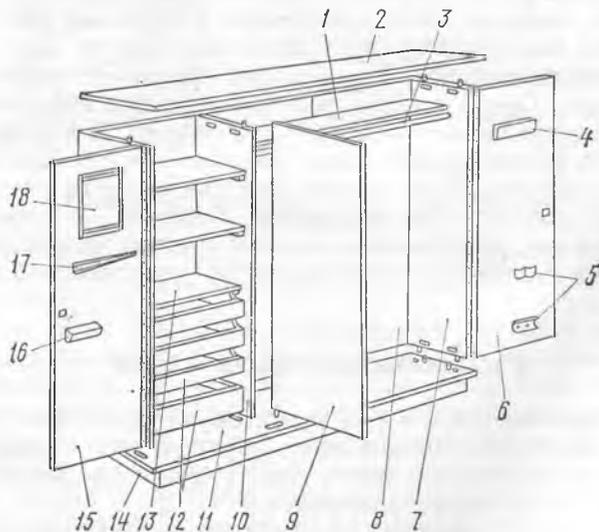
Конструкция трехдверного шкафа для платьев и белья:
